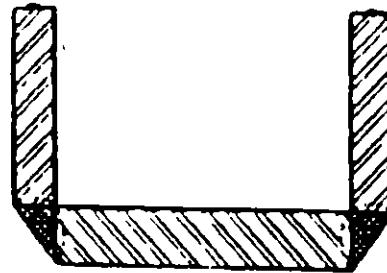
EJEMPLO DE SOLDADURA DE ESQUINA SOMETIDA A ESFUERZO FLEXIONANTE
